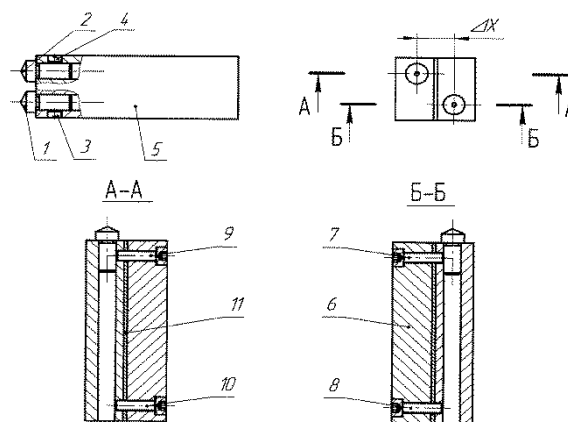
Выглаживатель с двумя рабочими элементами и регулировочной пластиной
